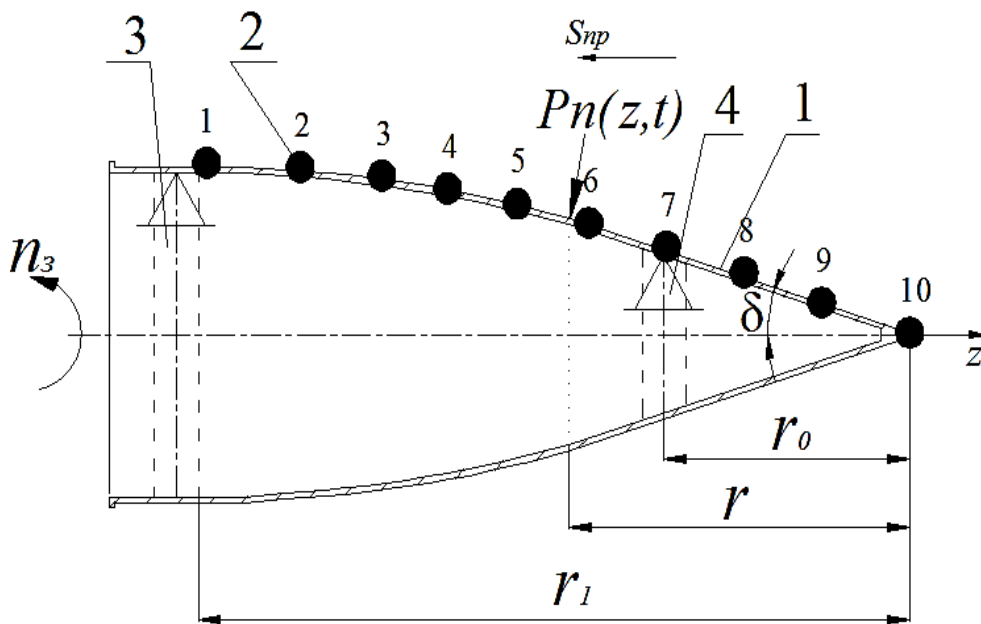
Схема к расчету колебаний стенки заготовки-оболочки
